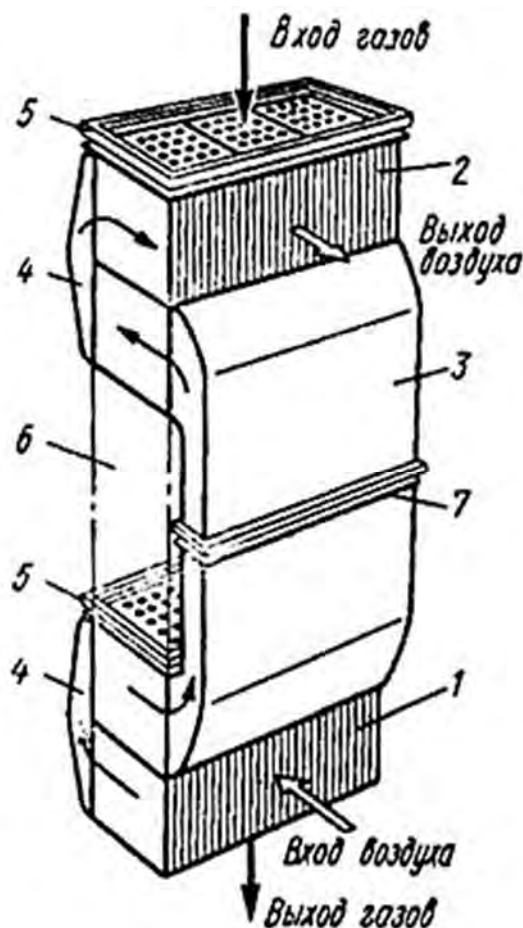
Рекуперативный воздухоподогреватель: 1 – нижние кубы воздухоподогревателя; 2 – верхние кубы воздухоподогревателя; 3, 4 – перепускные короба; 5, 7 – компенсаторы; 6 – место установки экономайзера
